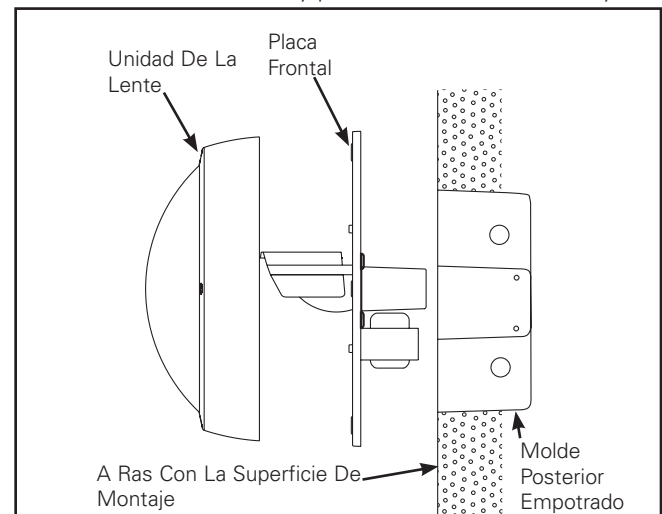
Unidad de lente y placa frontal Serie Harmony™
